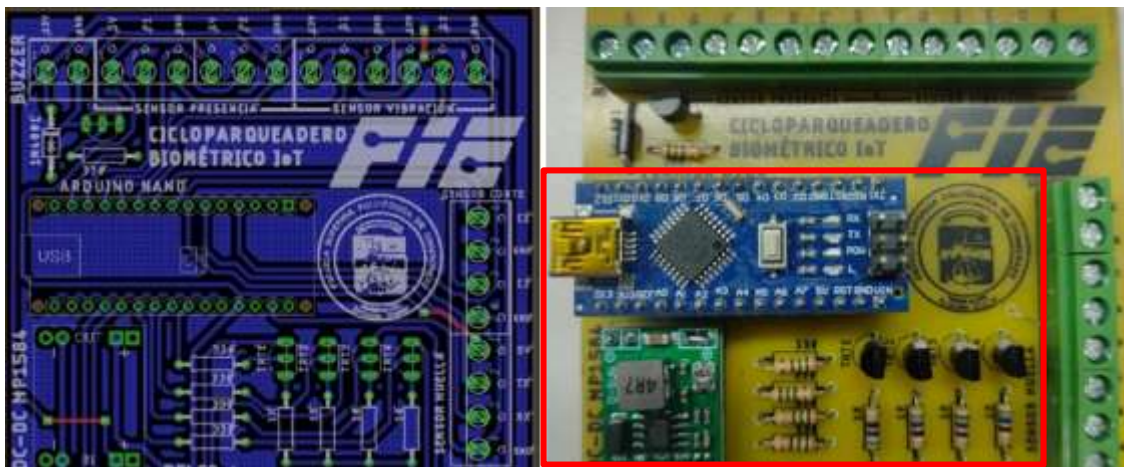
Diseño PCB y placa física del módulo de control y procesamiento.
